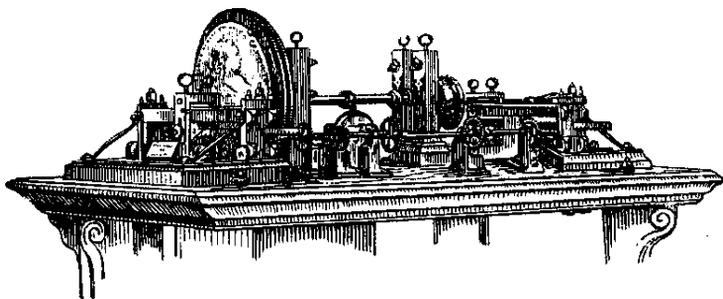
Токарно-копировальный медальерный станок Нартов: 1721 г. (общий вид).
